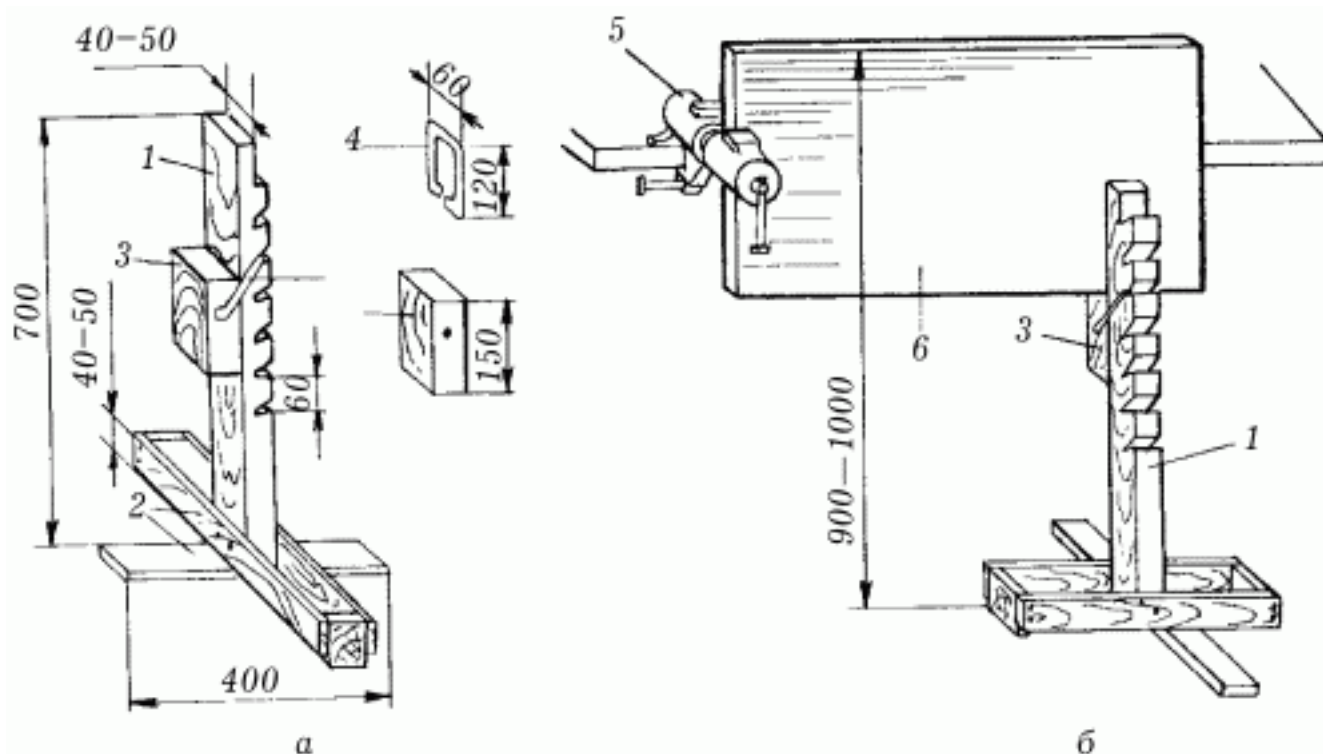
Подставка для опоры плиты при строгании (а) и закрепление обрабатываемой плиты (б): 1 – стойка; 2 – крестовина; 3 – ползун; 4 – скоба; 5 – тиски; 6 – плита.
